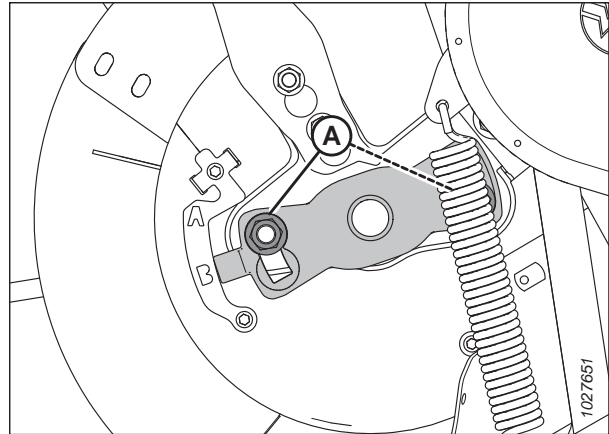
Zeiger für Einzugsfingersteuerung
